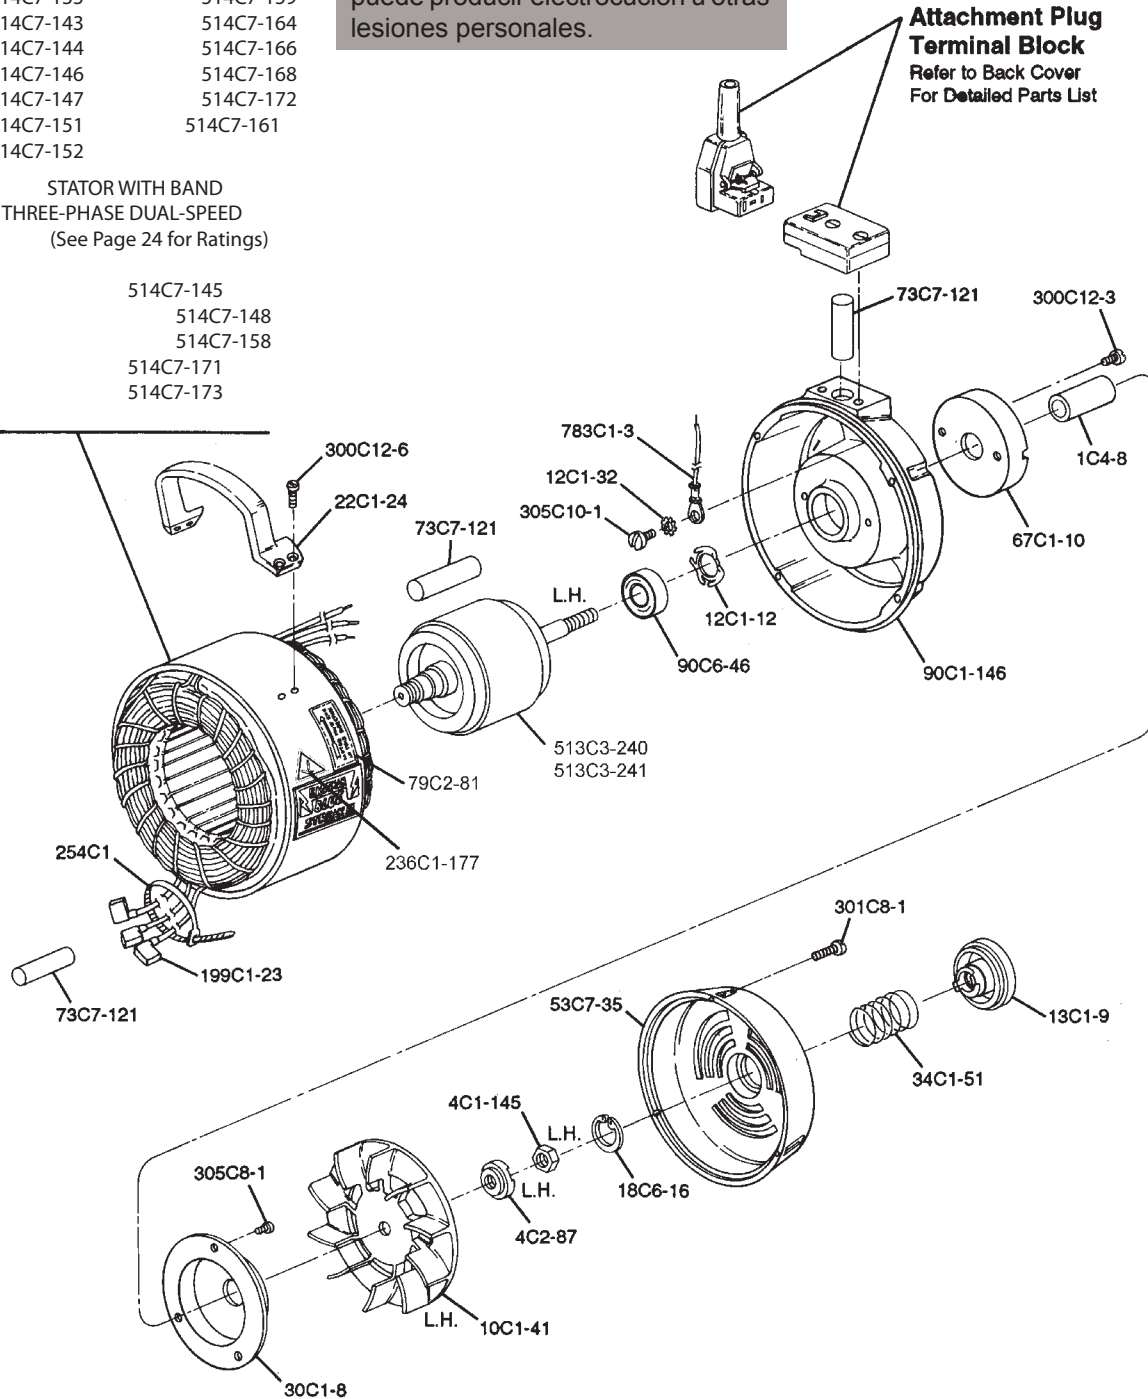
Motor Trifásico de Montaje (Vista Detallada)
